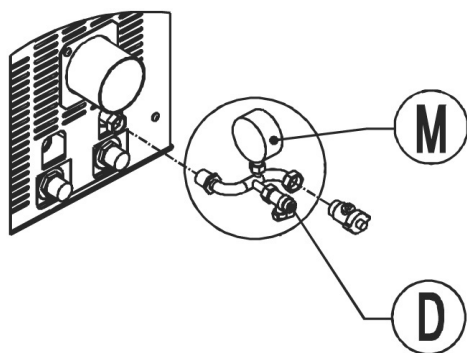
Terminal z zaworkiem załadunku (D) i mano-metr (M) (Akcesorium)
